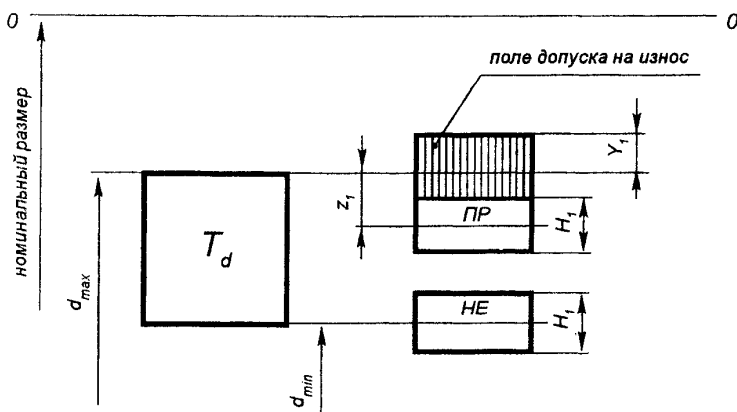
Схема расположения полей допусков калибров для контроля валов изготовленных по квалитетам 6, 7 и 8 при номинальных размерах до 180 мм (для размеров валов изготовленных по квалитетам от 8 до 17,  $Y = 0$ )
